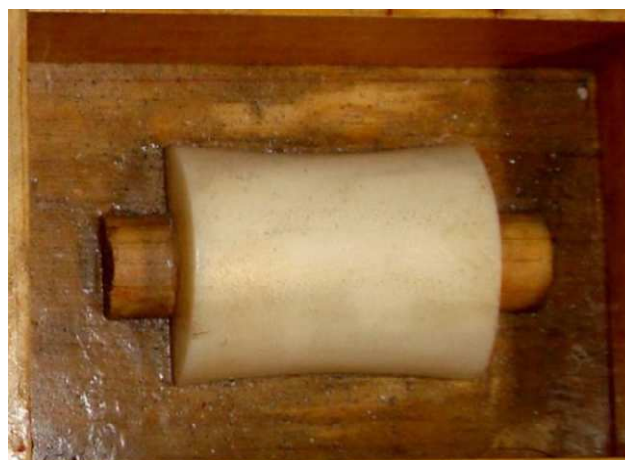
Mitad de la pieza fijada sobre una placa de madera para hacer la base del molde para la resina.
